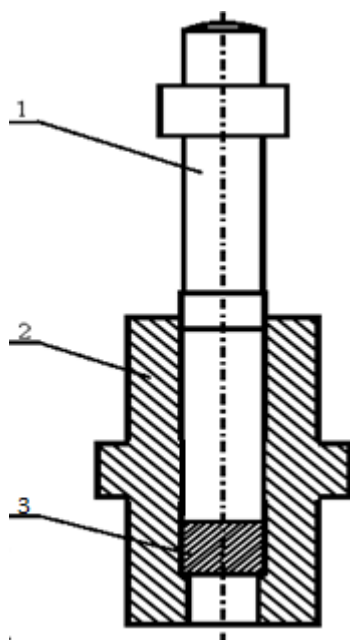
Пресовий пристрій для виготовлення пелет в закритій матриці
